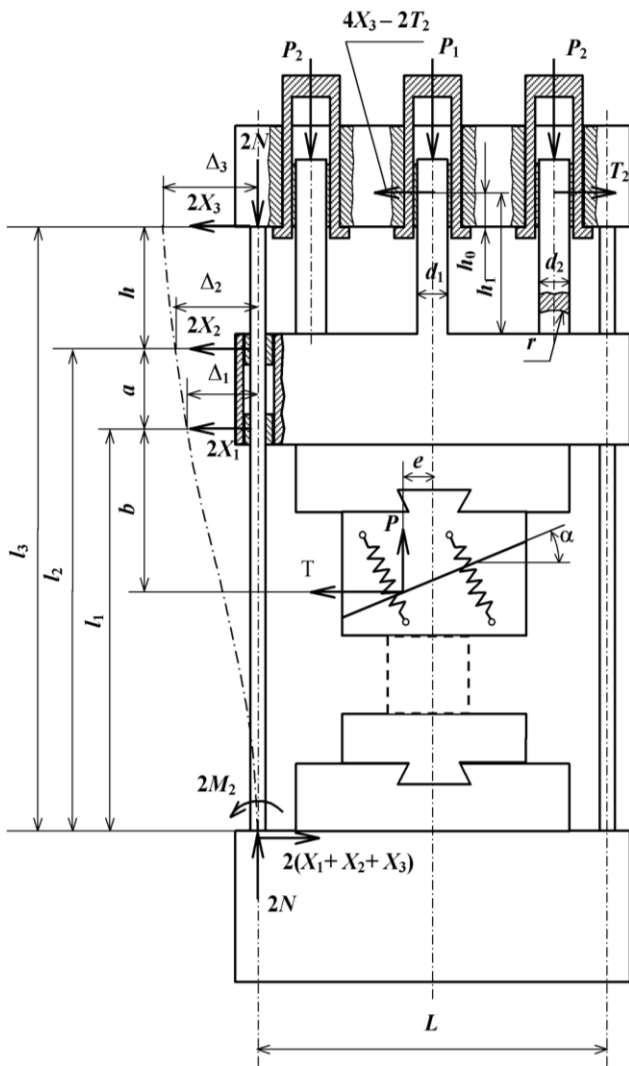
Схема работы и размеры элементов пресса при поперечном сдвиге заготовки
